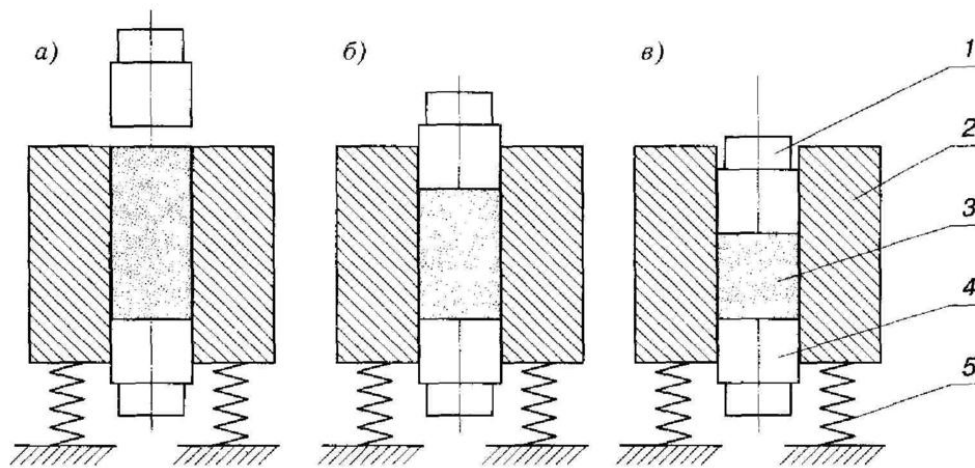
Стадії пресування в плаваючій формі:
